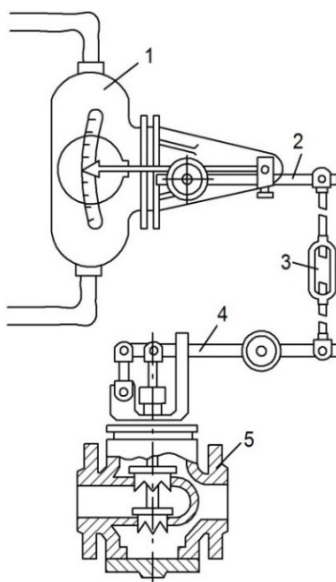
Поплавковый камерный регулятор уровня: 1 – камера; 2, 4 – рычаг; 3 – тяга; 5 – регулирующий клапан
